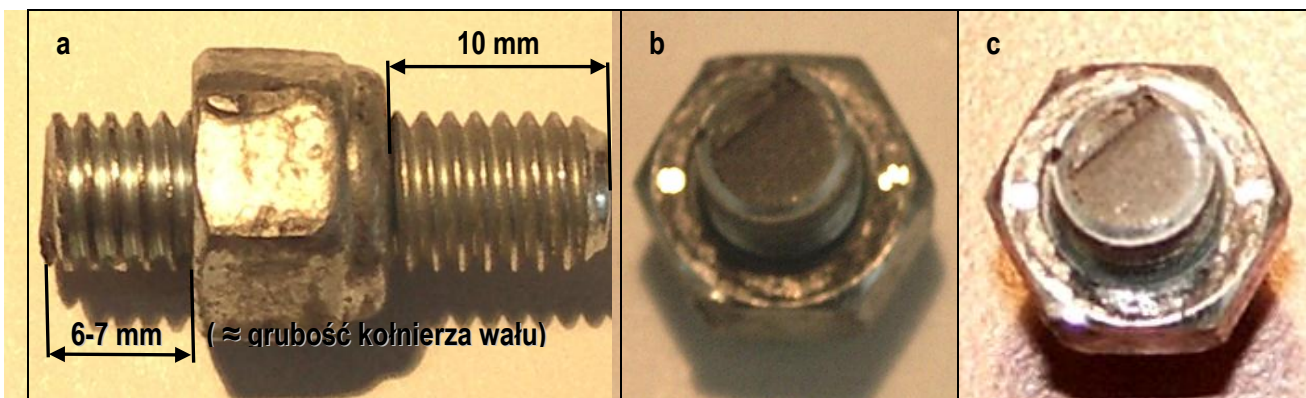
Piasta śmigła – montaż do kołnierza wału silnika.
